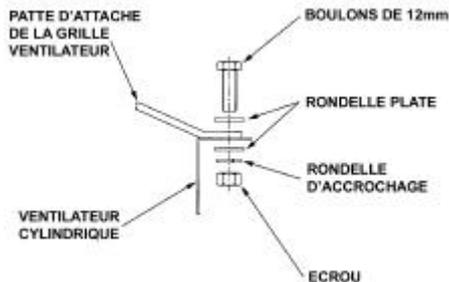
Fixation de la grille de protection ventilateur sur le cylindre
